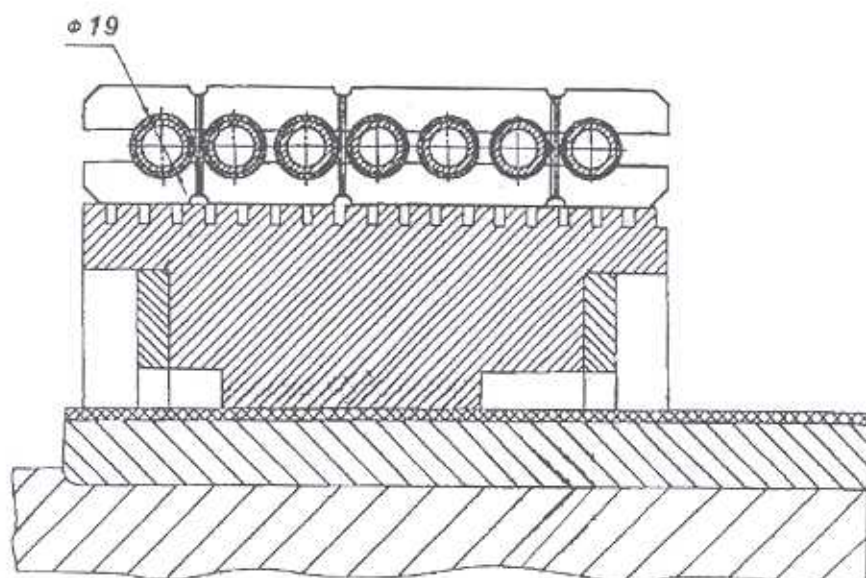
Установка индуктора для нагрева контактного кольца
